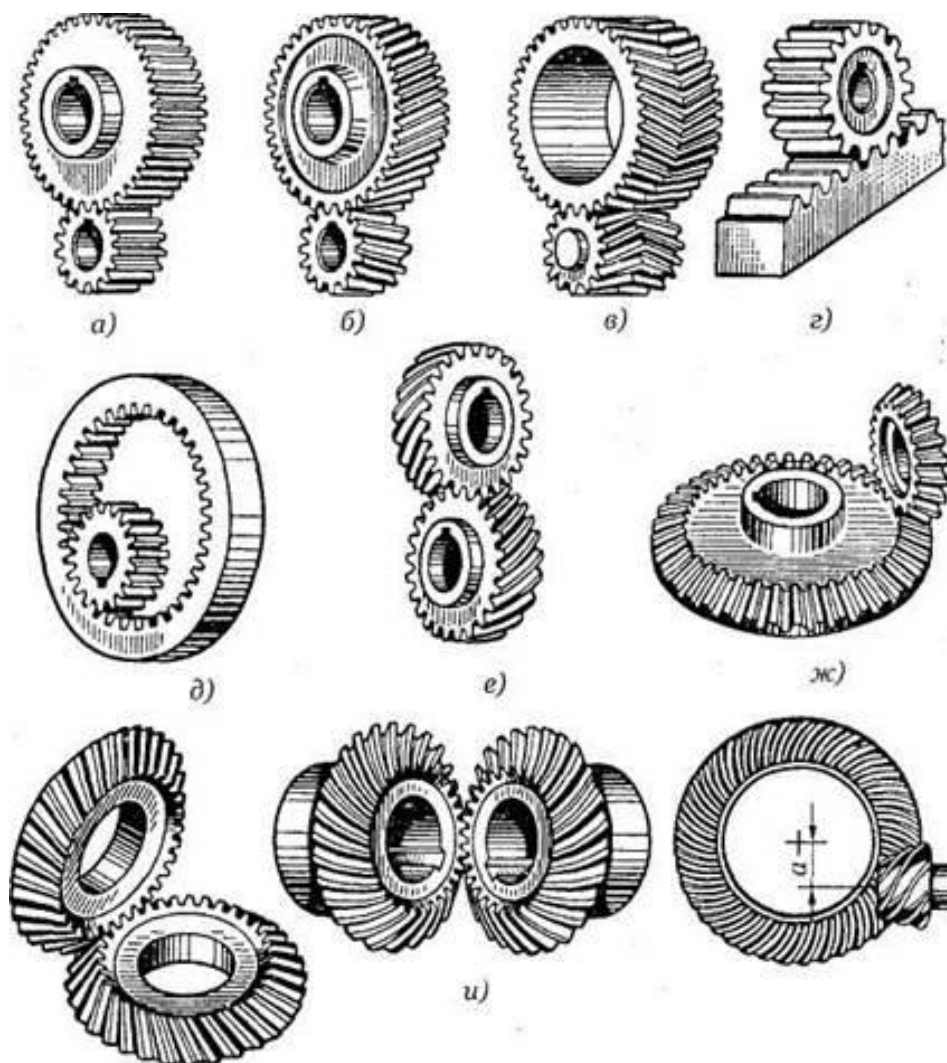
Види зубчастих передач: *a, б, в* – циліндричні зубчасті передачі із зовнішнім зачепленням; *г* – рейкова передача; *д* – циліндрична передача із
